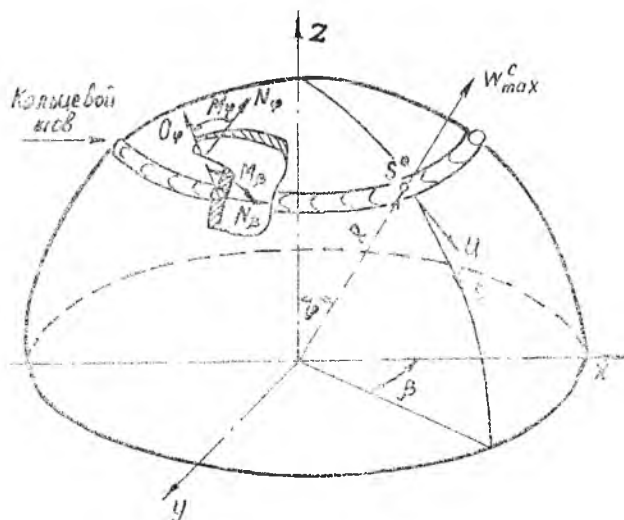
Сферическая оболочка с круговым сварным швом
